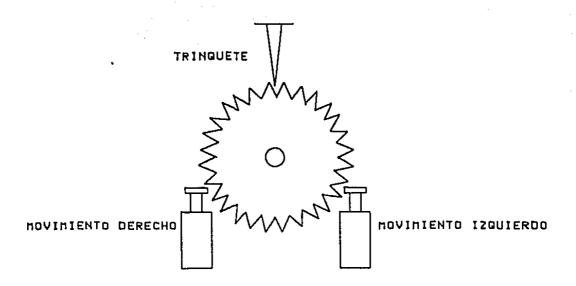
MOTOR DE SOLENOIDE Y TRINQUETE
